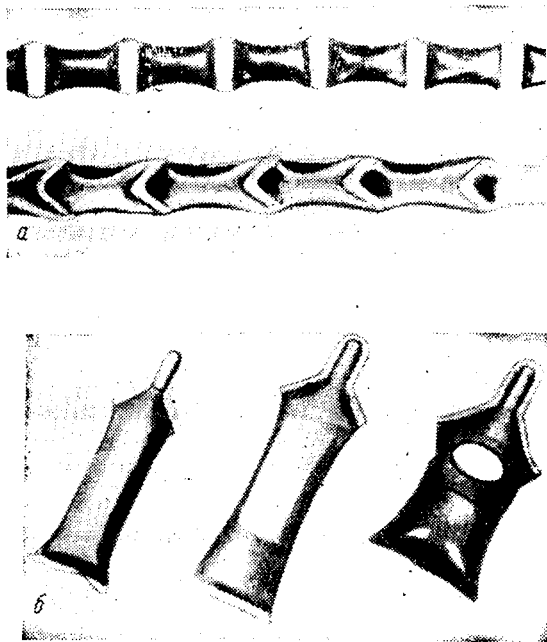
Виды упаковки, изготовленной из полихлорвиниловой пленки токами высокой частоты:
